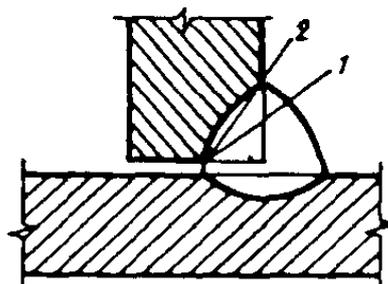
Схема расчетных сечений сварного соединения с угловым швом
